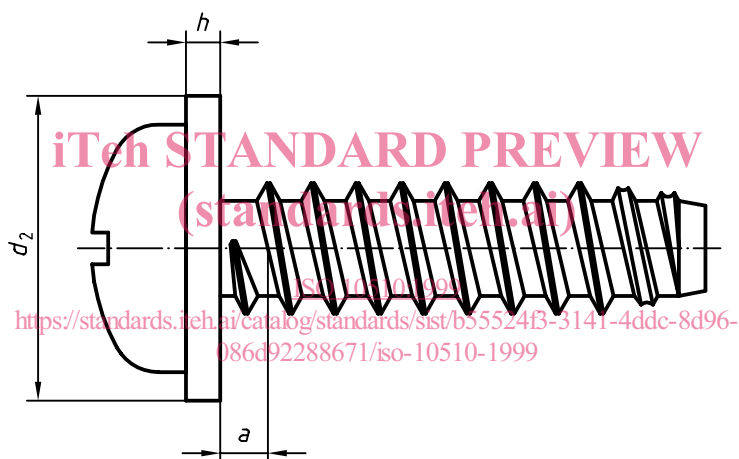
Vis à tôle à tête cylindrique bombée large à bout plat
